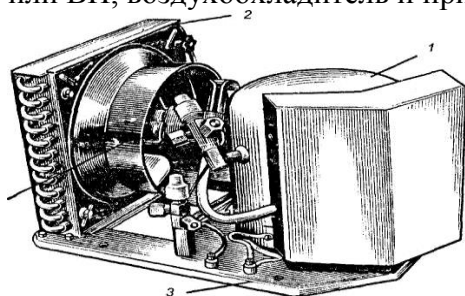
Холодильный агрегат ВС 400-1 [2]: 1 — герметичный компрессор; 2 — конденсатор; 3 — штампованная плита; 4 — диффузор
